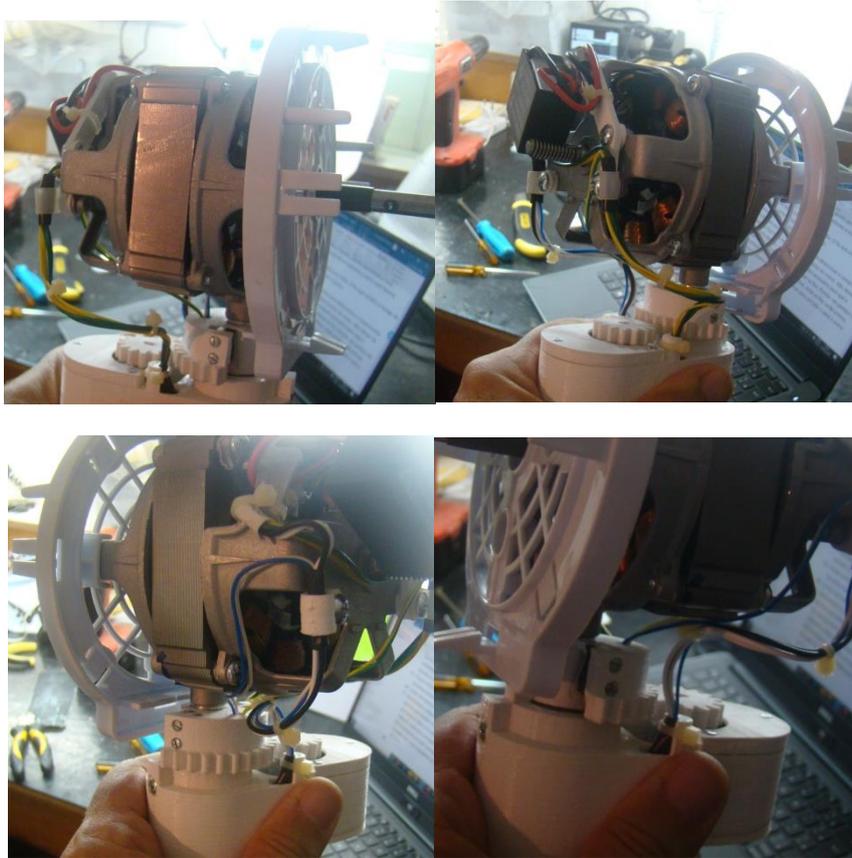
Passagem e fixação dos dois conjuntos de fios que vão descer para a o compartimento vertical.
